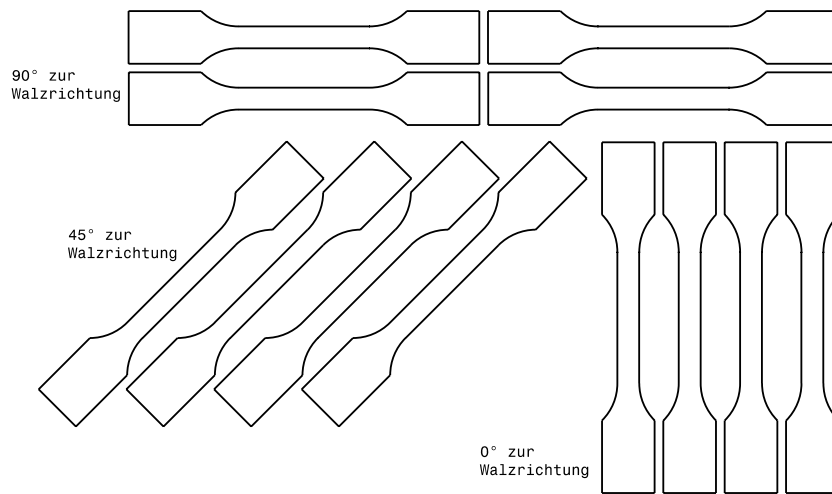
Skizze für die Entnahmeposition der Proben
